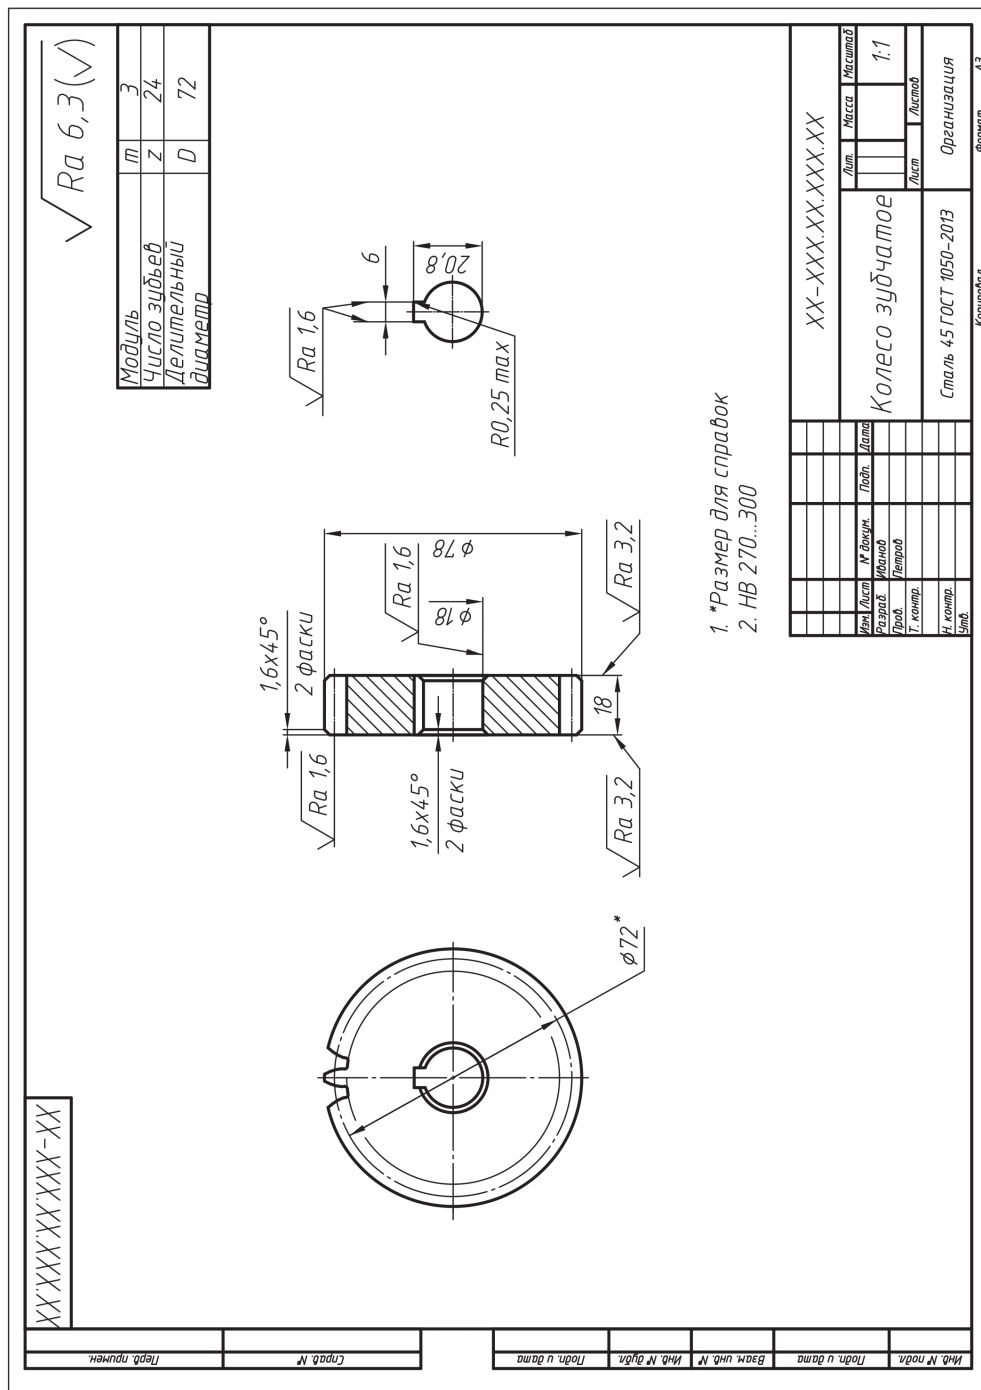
Пример выполнения учебного чертежа детали «Колесо зубчатое» на формате А3
